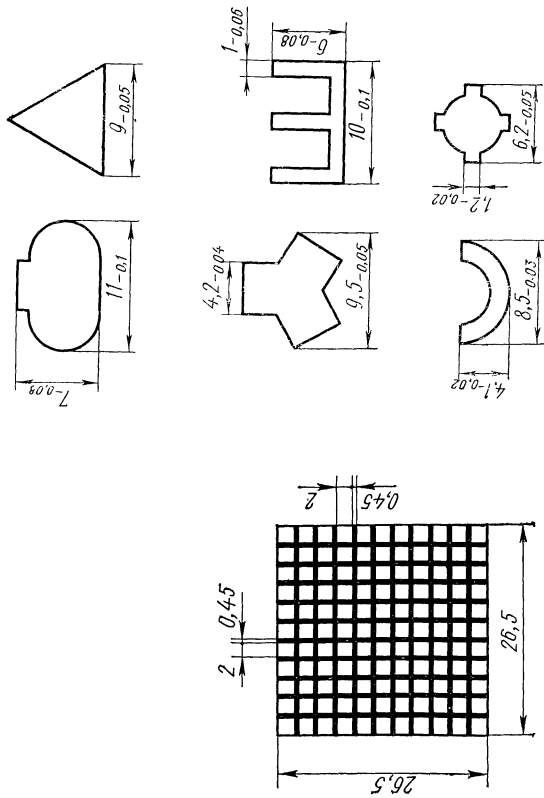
Схема раскроя плоской заготовки на квадратные элементы
